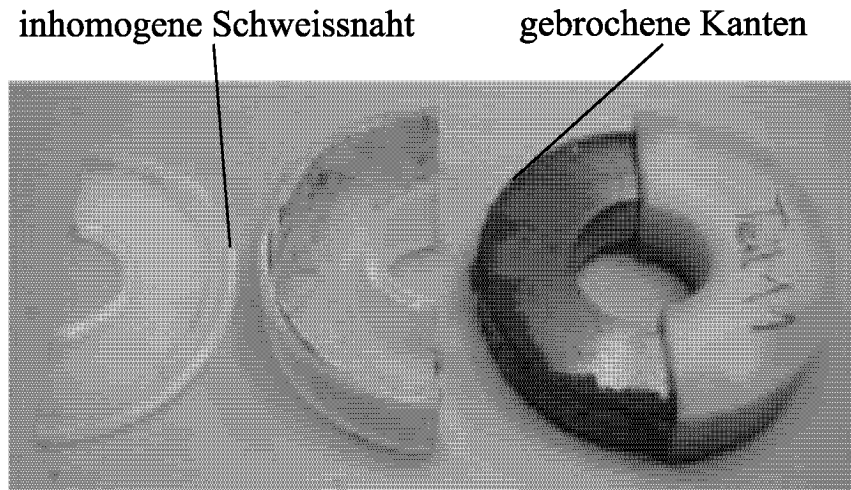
Mit Ultraschall verschweisste Rotorummantelung
